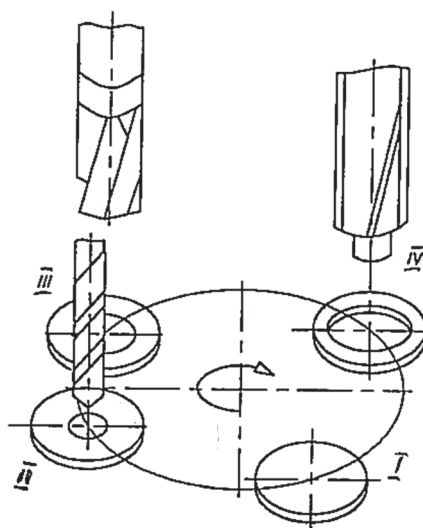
Схема четырехпозиционной обработки заготовки на многошпиндельном вертикально-сверлильном станке
